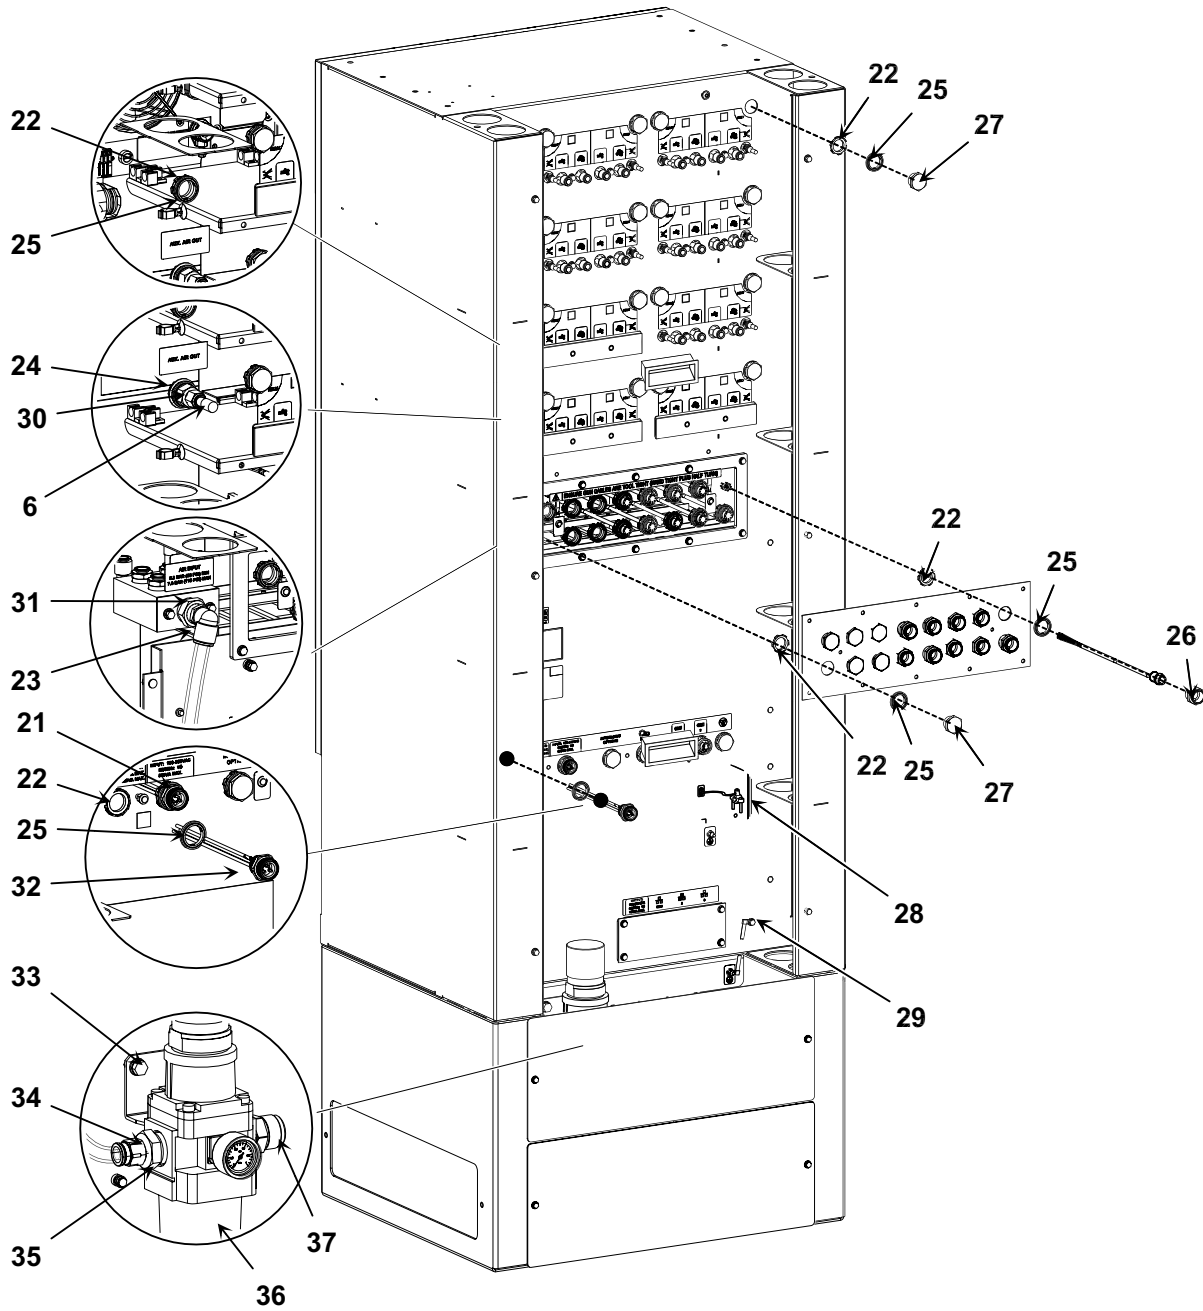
Komponenten der Zusatzsteuerung mit Kühlgerät, 2 von 2
